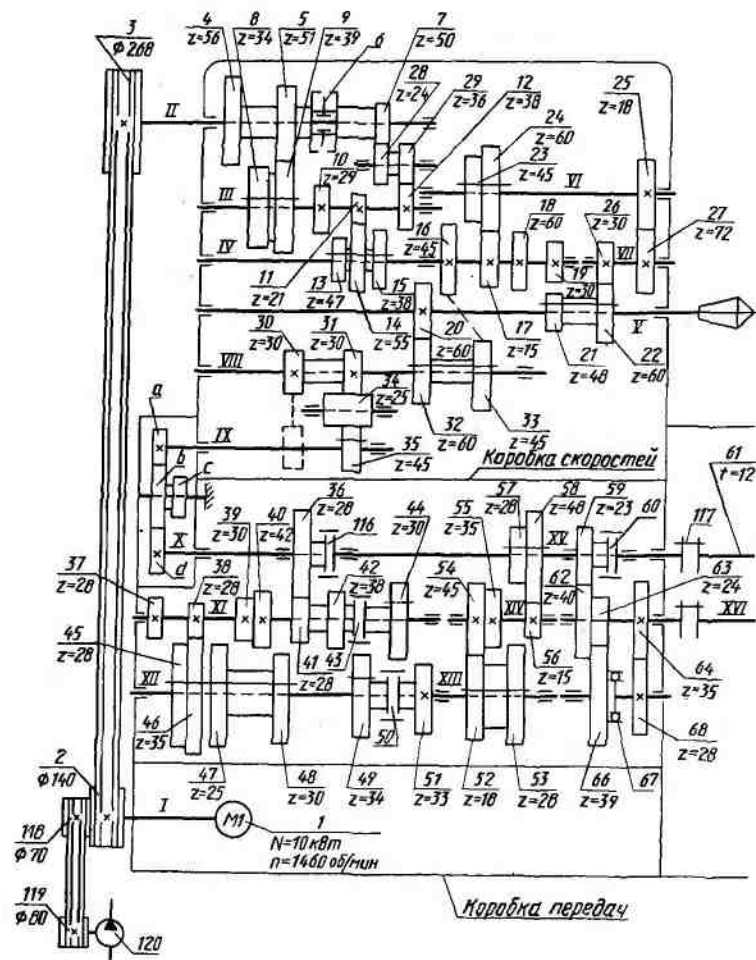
Кинематическая схема коробки скоростей и коробки подач станка мод. 16K20
